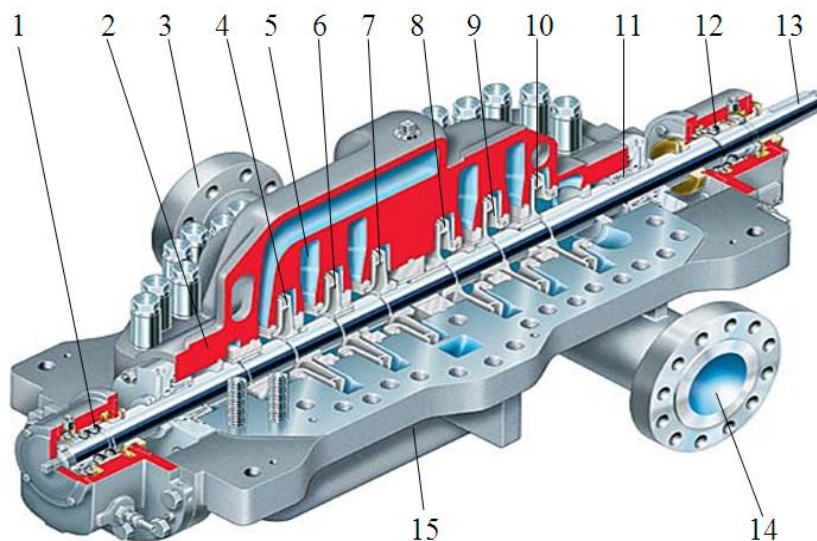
Центробежный многоступенчатый горизонтальный насос с осевым разъемом корпуса типа ЦН (М):
